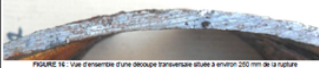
Vue d'ensemble d'une découpe transversale située à environ 200 mm de la rupture (épaisseur résiduelle 10 mm sur de plan : 4,5 mm).
